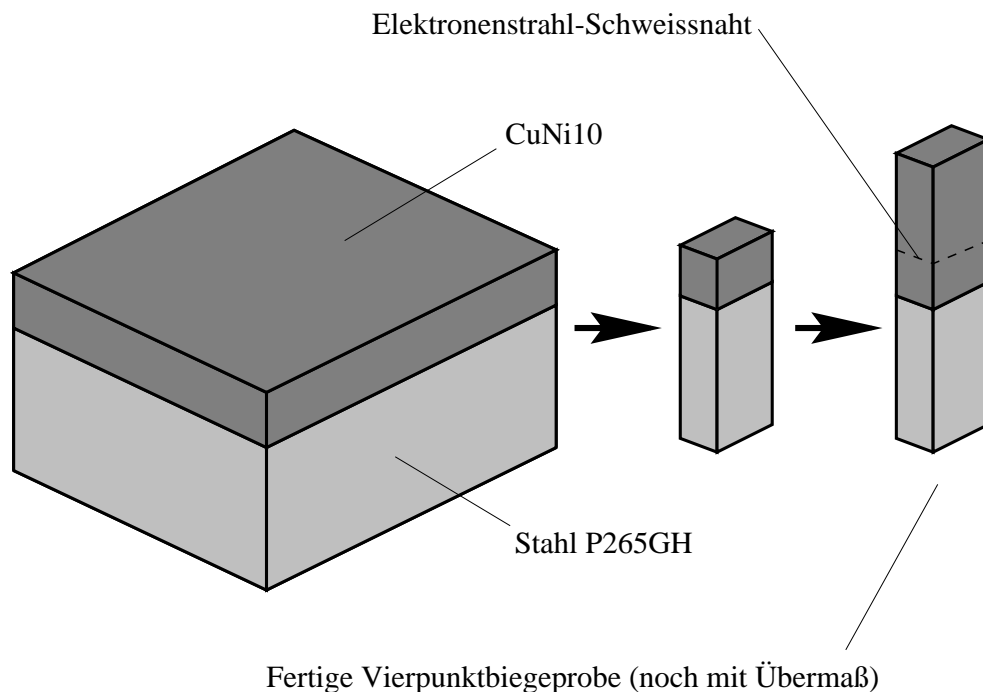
Herstellung einer Bimaterial-Vierpunktbiegeprobe aus einer explosionsgeschweißten Platte
